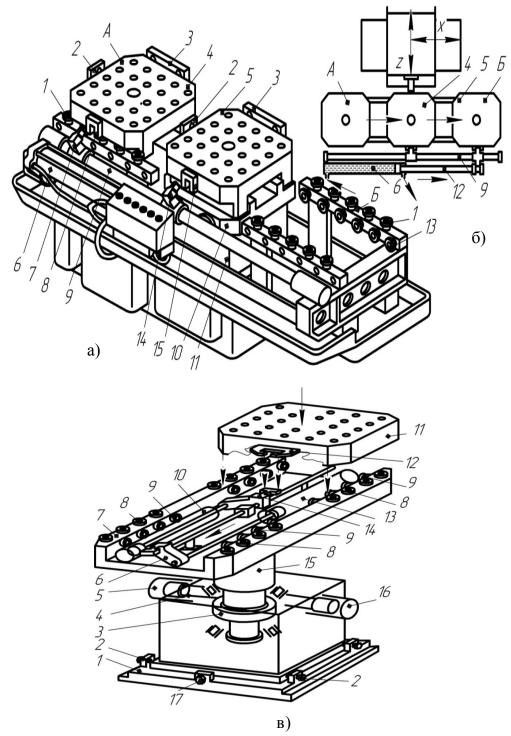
Устройство автоматической смены спутников: а, б) 1, 13 — ролики; 2, 3 — планки; 4, 5 — плиты-спутники; 6 — гидроцилиндр; 7, 14 — захваты; 8, 15 — замки; 9 — каретка; 10 — стол; 11 — станина; 12 — шток; в) 1 — плита; 2, 17 — болты; 3 — зубчатое колесо; 4 — рейка; 5, 10, 13, 16 — гидроцилиндры; 6, 14 — захваты; 7 — стол; 8, 9 — ролики; 11 — спутник; 12 — вырез фигурный; 15 — стойка
